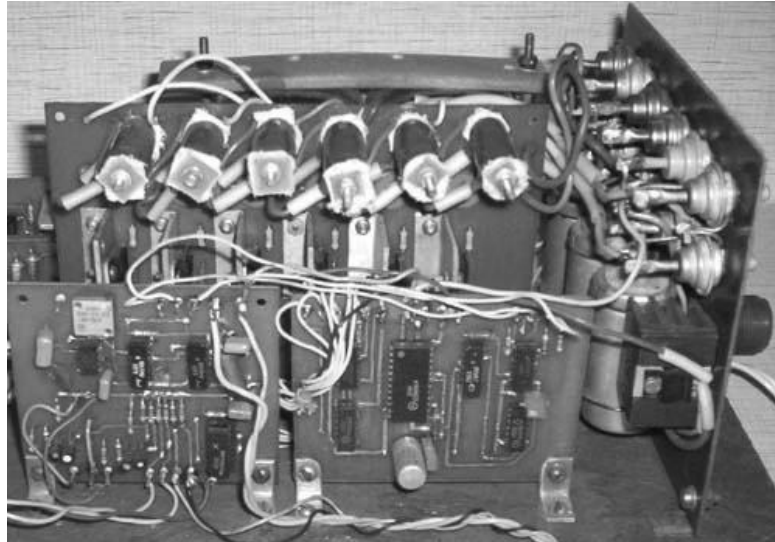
Типова конструкція контролера керування потужним кроковим двигуном у зборі
